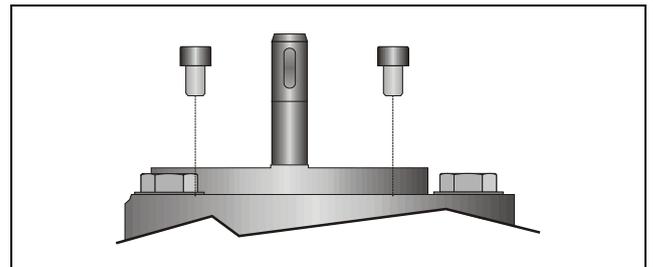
Desserrage et retrait des vis à tête cylindrique
